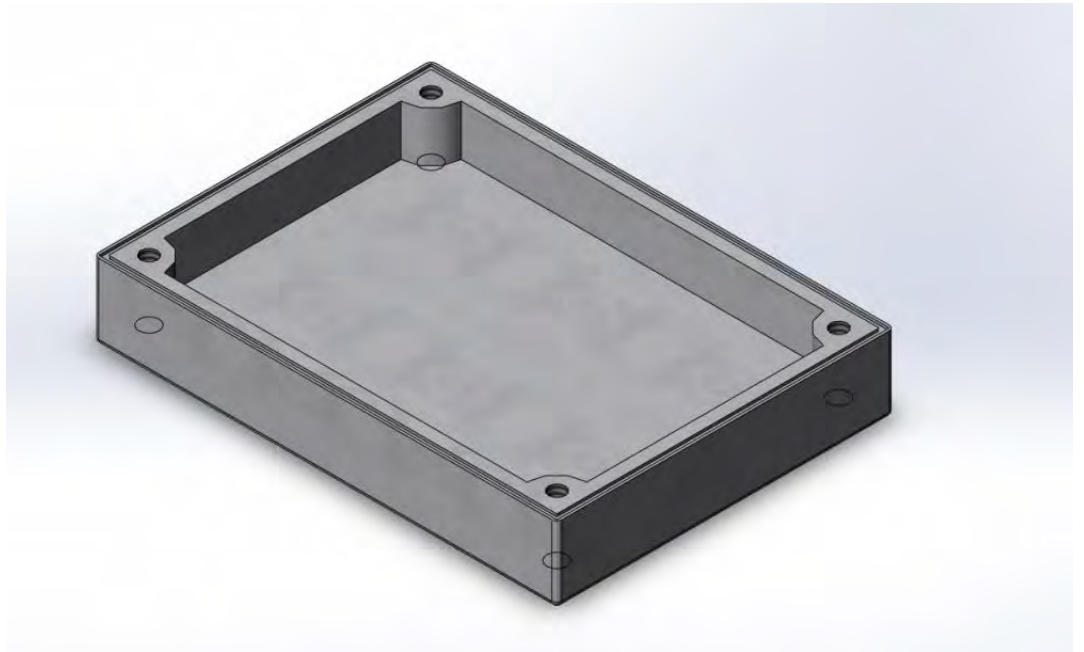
Зображення моделі верхньої кришки корпусу
